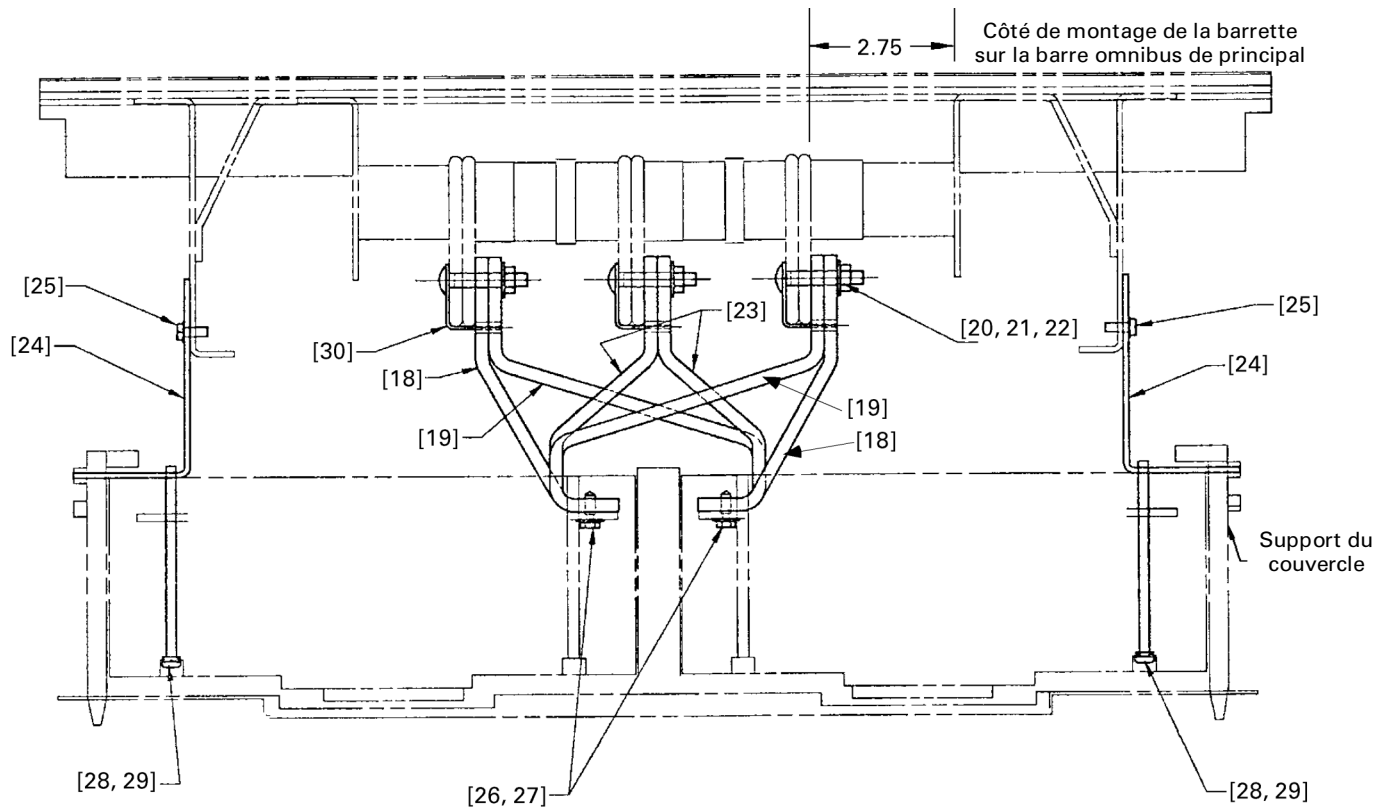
Assemblage de disjoncteur double avec boulonnage, vue du bout.
